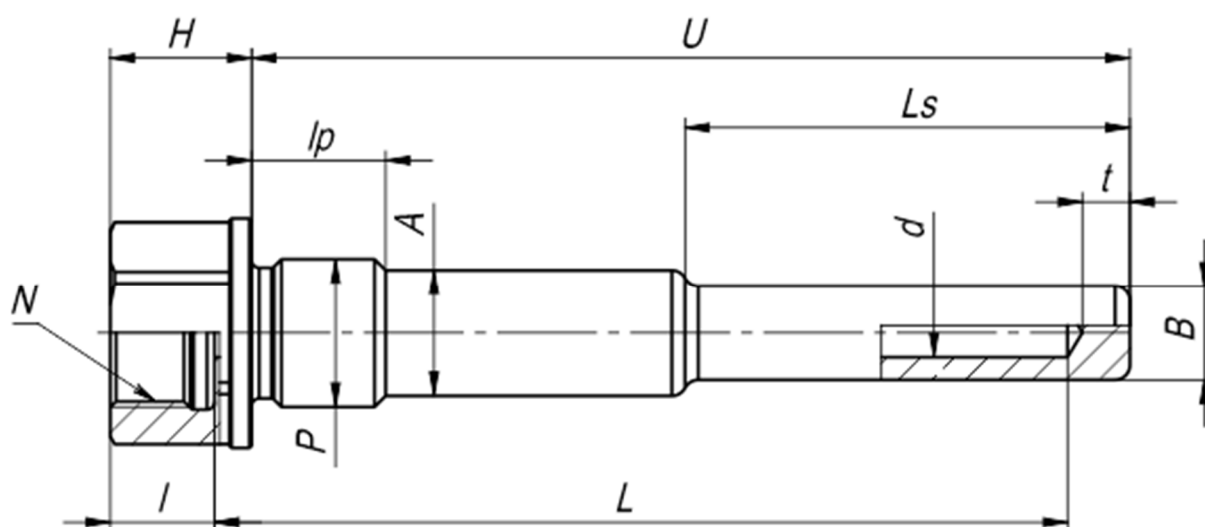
Гильза резьбовая, цельноточёная, ступенчатая под подвижный шуцер.
